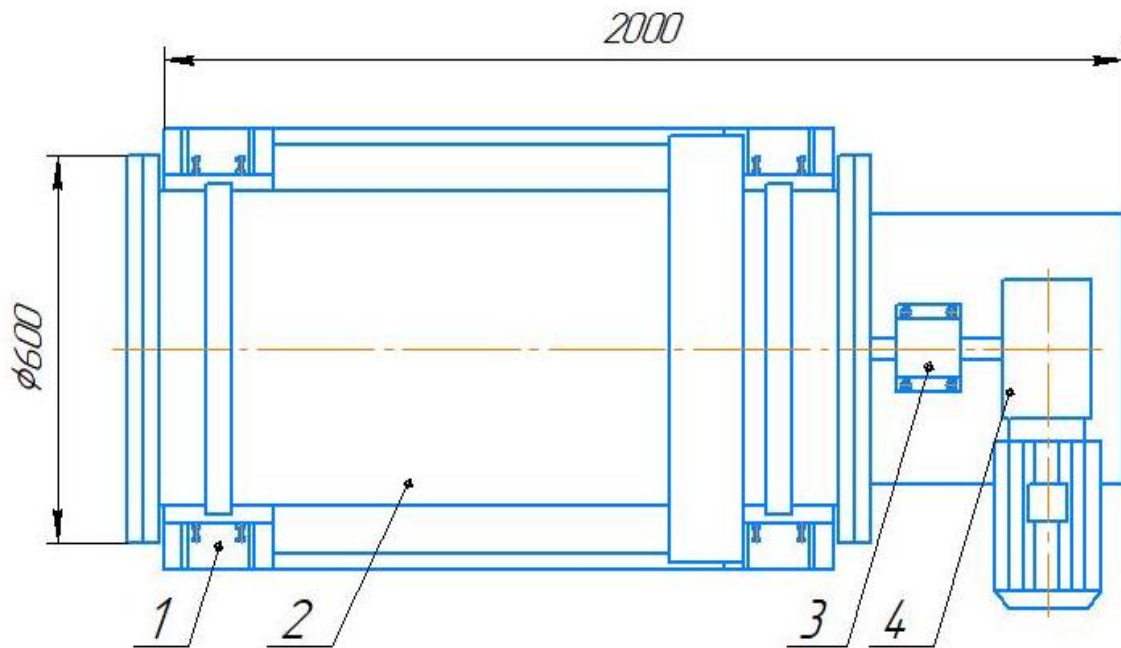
Барабанный смеситель-окомкователь аглодоменной лаборатории АО «Уральская Сталь» после модернизации: 1-рама; 2-барабан; 3-муфта с кожухом; 4-мотор-редуктор
